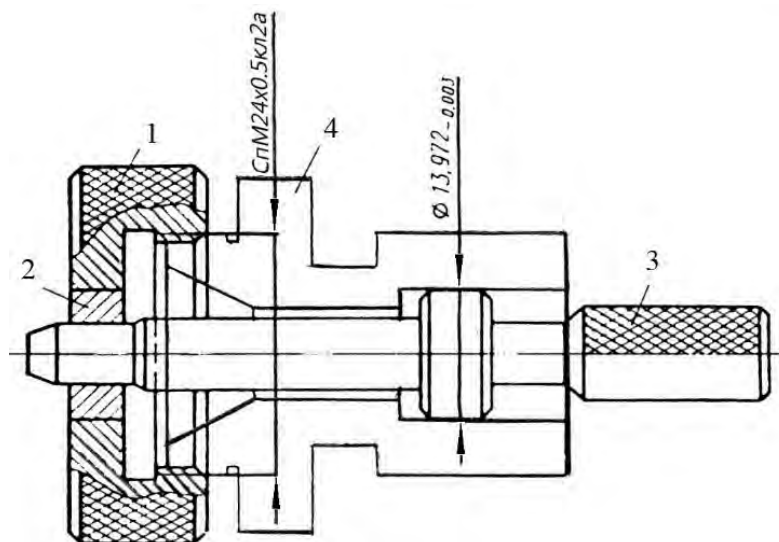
Калибр для контроля биения поверхностей оправы
